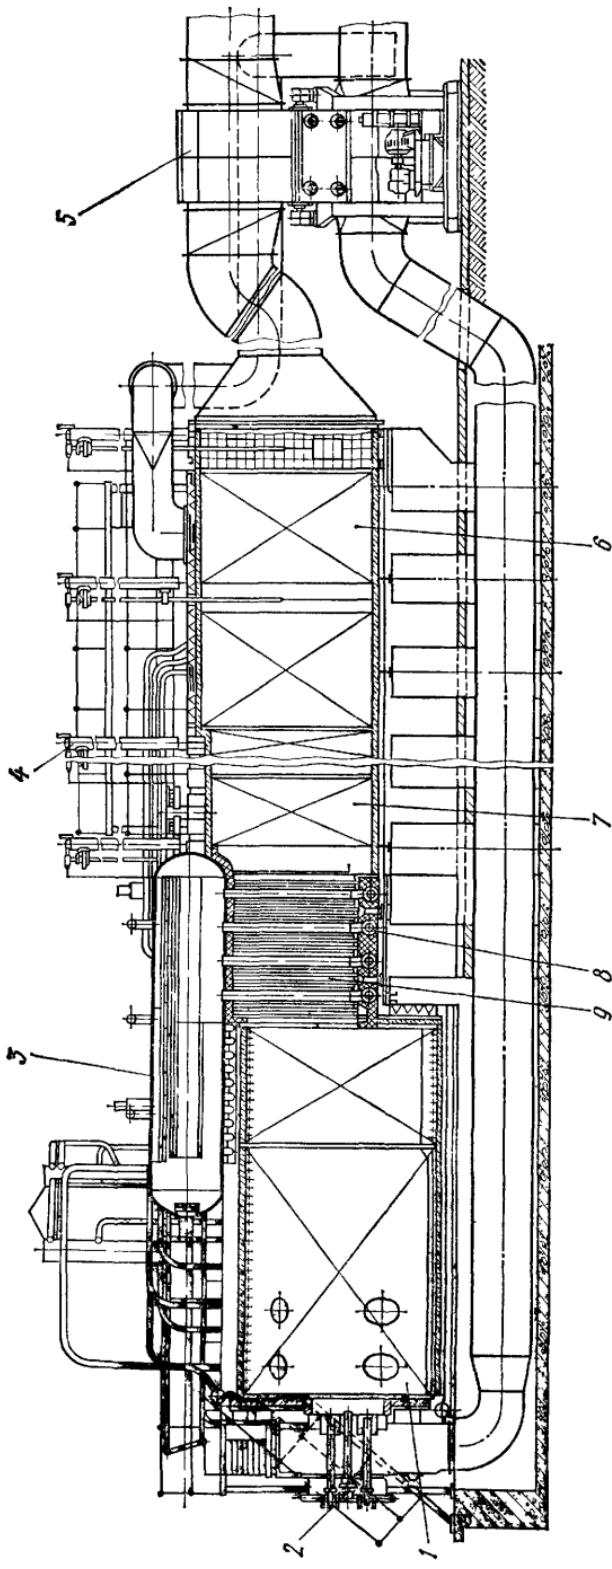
Газомазутный котлоагрегат ГМН-75:
